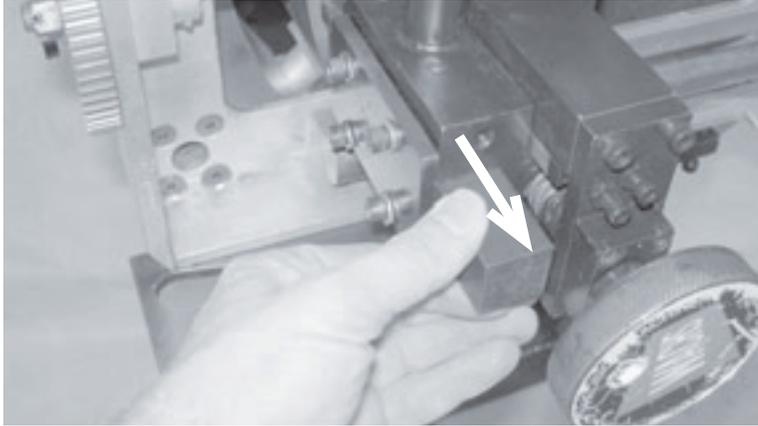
Ziehen Sie die Schrauben an, mit denen die Schablone befestigt ist.
